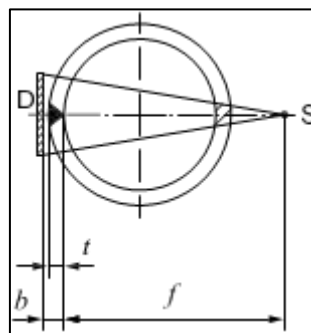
Arranjo para parede dupla vista simples em soldas longitudinais.
